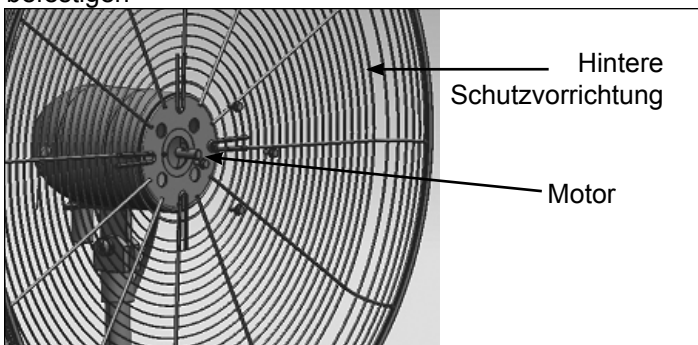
Hintere Schutzvorrichtung am Motor befestigen
